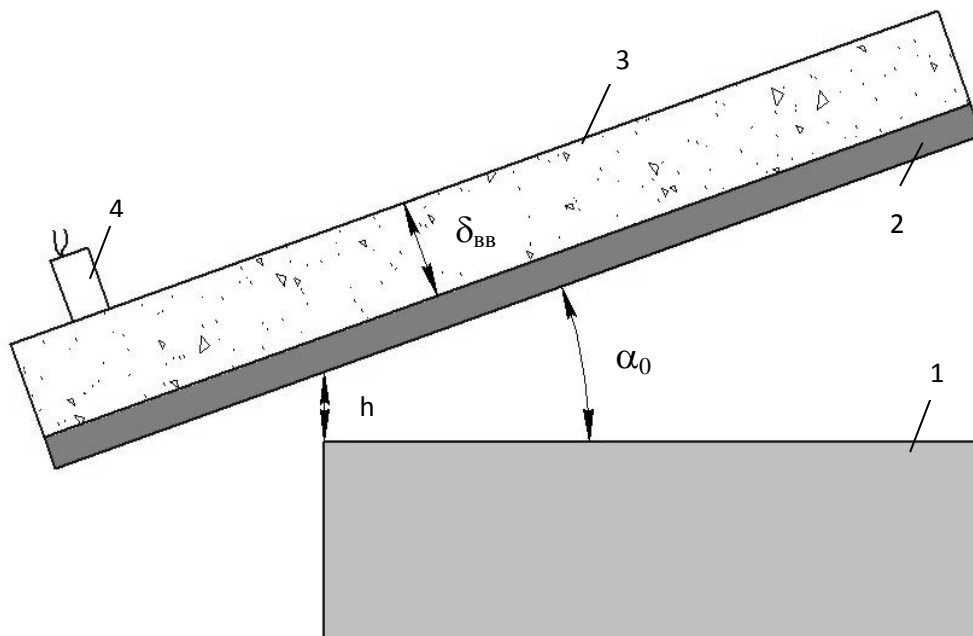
Схема сварки взрывом: 1 - плакируемая пластина; 2 - метаемая (плакирующая) пластина; 3 – заряд взрывчатого вещества; 4 – детонатор [4]
